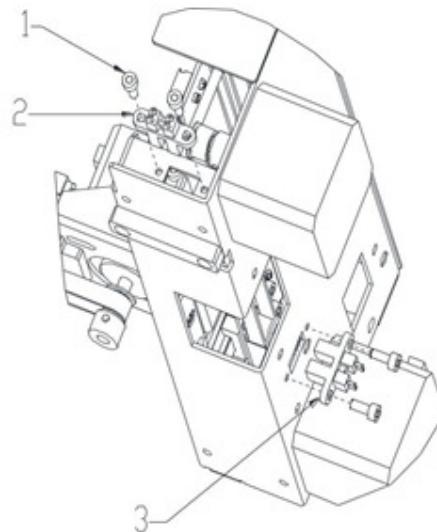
Conjunto de mistura removendo o optoacoplador de deflexão
